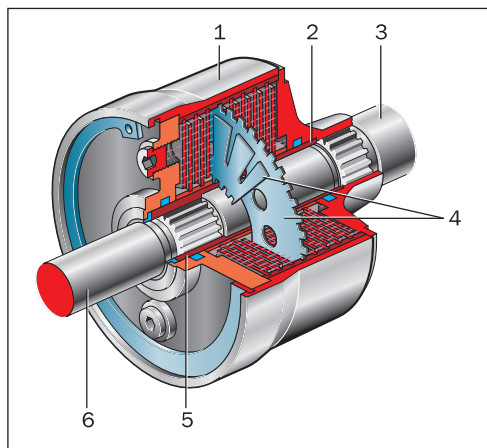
Устройство вязкостной муфты (вискомуфты): 1 — корпус; 2 — вал корпуса; 3, 6 — ведущий и ведомый валы; 4 — диски; 5 — уплотнения
